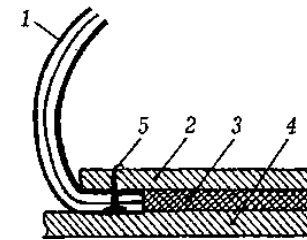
Клеевой метод крепления подошвы: 1 – заготовка; 2 – основная стелька; 3 – простилка; 4 – подошва; 5 – натяжные гвозди (тексы)
